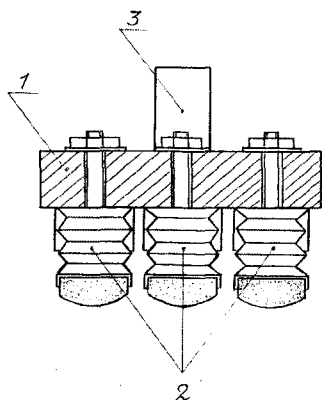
Круг, состоящий из множества сильфонов несущих одинаковые шлифовальные головки, бруски: 1 - основание круга; 2 - сильфоны с направляющими цилиндрами и наконечниками, закрепленными в основании круга, несущие шлифовальные головки; 3 - наконечник крепления круга в станок.
